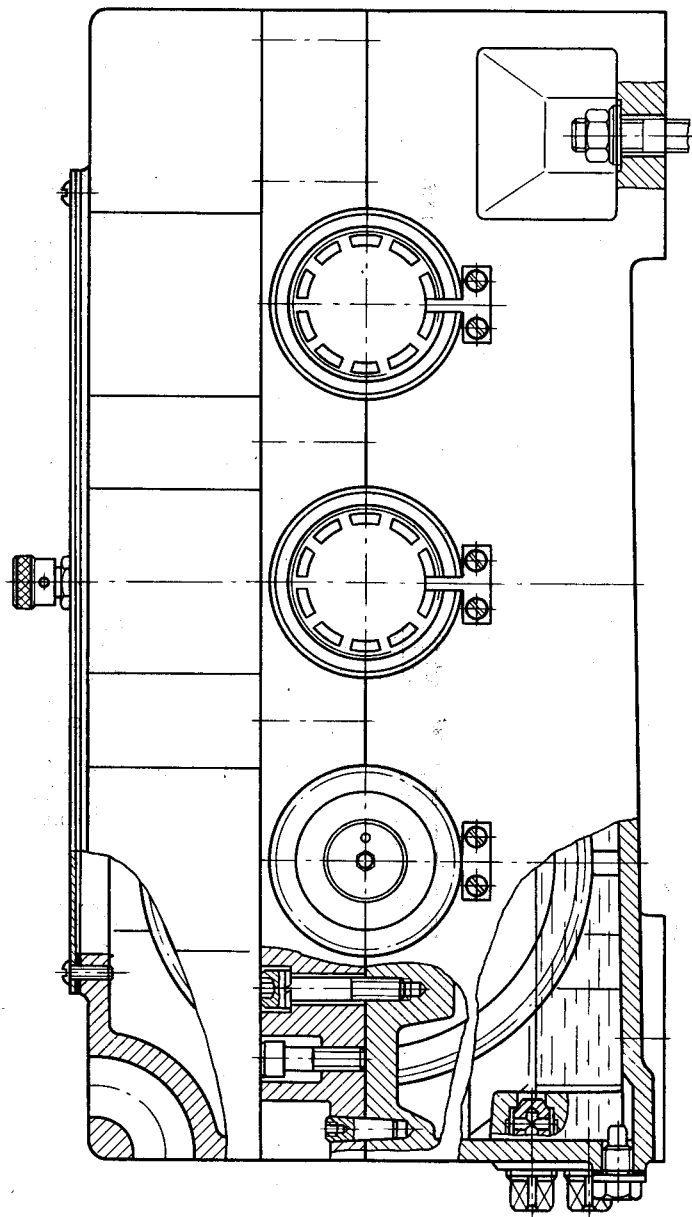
Редуктор цилиндрический одноступенчатый горизонтальный (с двумя тихоходными валами)
